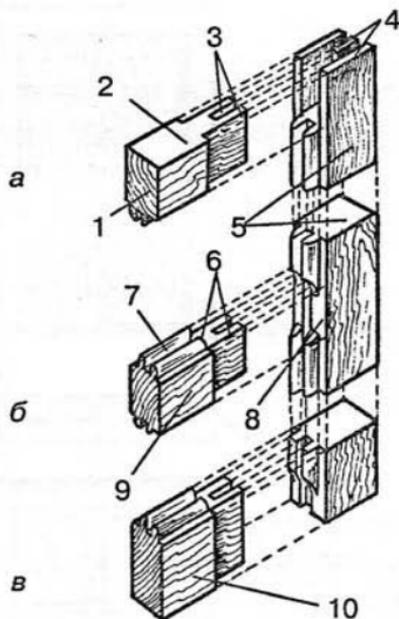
Детали филенчатой двери: а — вязка верхнего узла; б — вязка средника; в — вязка нижнего узла: 1, 7 — паз; 2 — верхний брусок обвязки; 3, 6 — шпты; 4 — проушина; 5 — боковой брусок обвязки; 8 — гнездо; 9 — средник; 10 — нижний брусок обвязки
